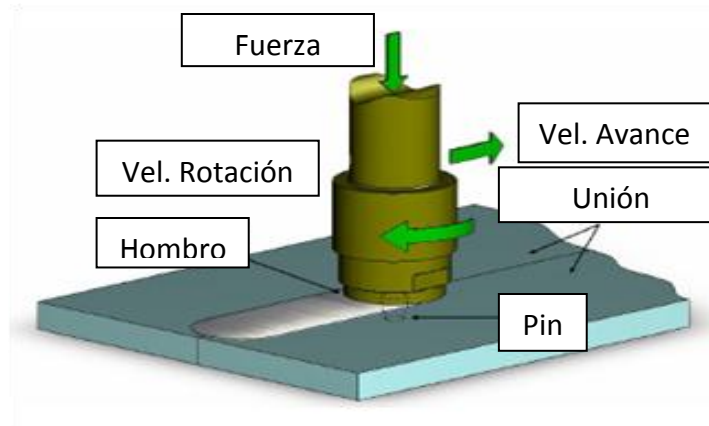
Esquema del proceso de soldadura (FSW). Adaptado de Capelari & Mazzaferro (2006).
